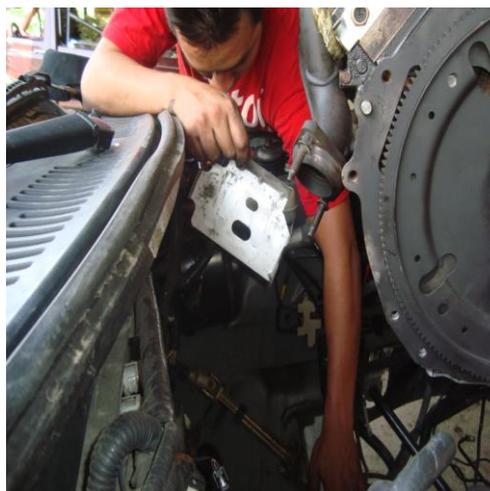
Posición del motor para instalarlo. Fig.4.24 Posición de soportes.
